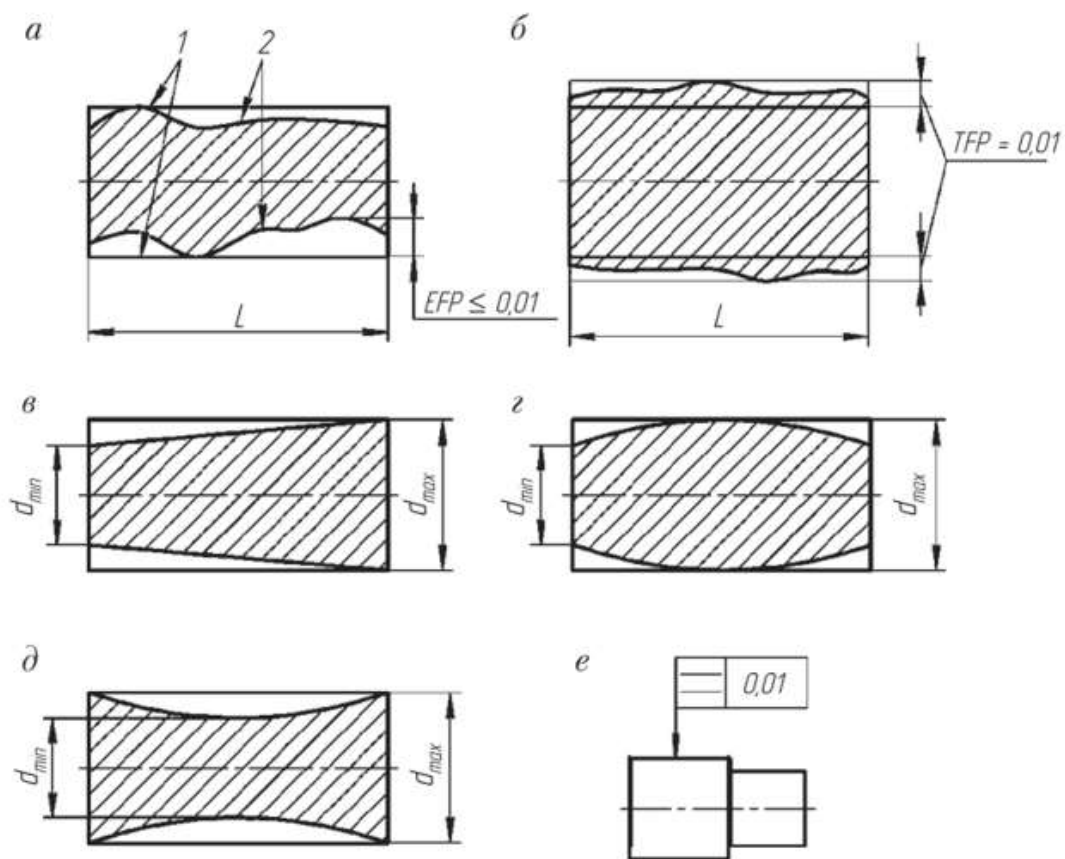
Схема визначення: а – відхилень профілю поздовжнього перерізу; б – поля допуску; в,г,д - окремих випадків; е – приклад позначення на кресленнях; 1- прилеглий циліндр; 2 – реальний циліндр.
